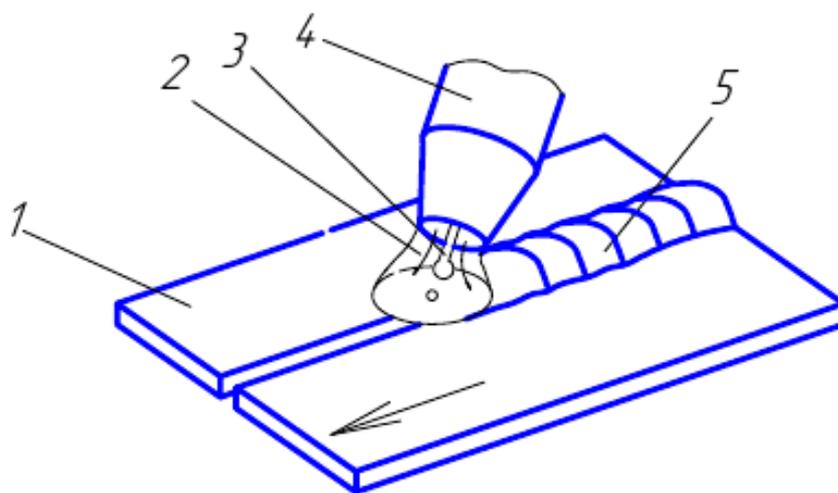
Схема сварки проволокой в защитных газах:
